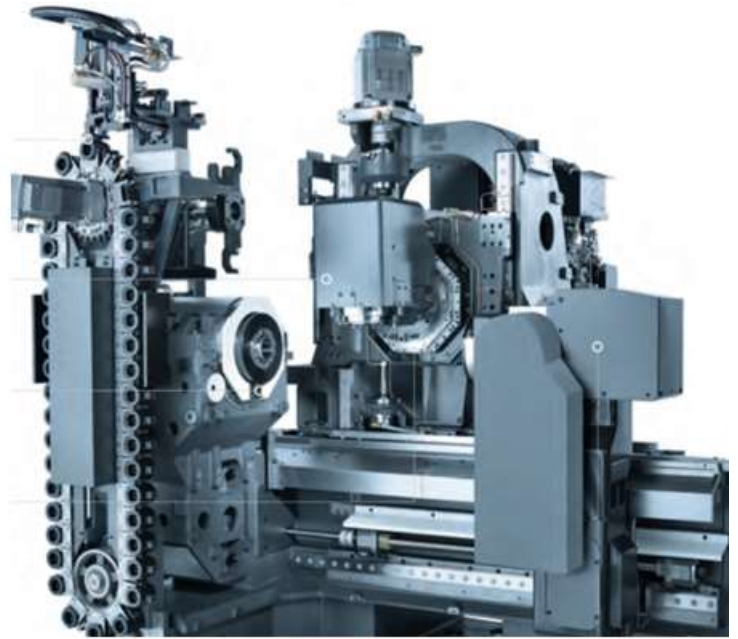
Високоточний гнучкий модуль на базі обробного центру NTX 1000 www.dmgmori-seiki.com
